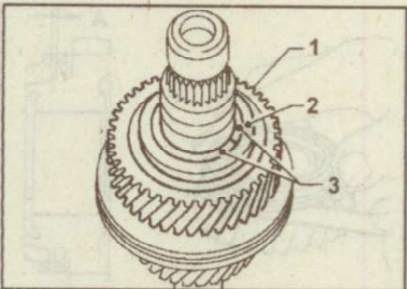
Установка шестерни 4-й передачи (1), упорных шайб (3) и кольца (2)
